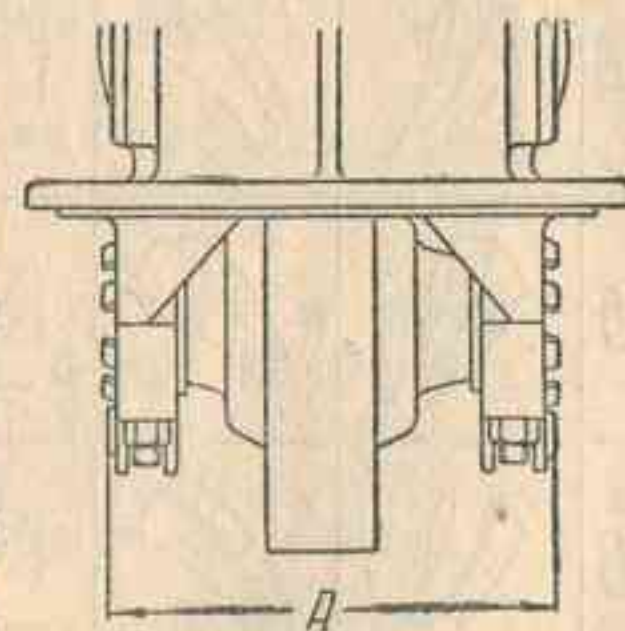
Размер, проверяемый при регулировке затяжки подшипников коробки дифференциала
